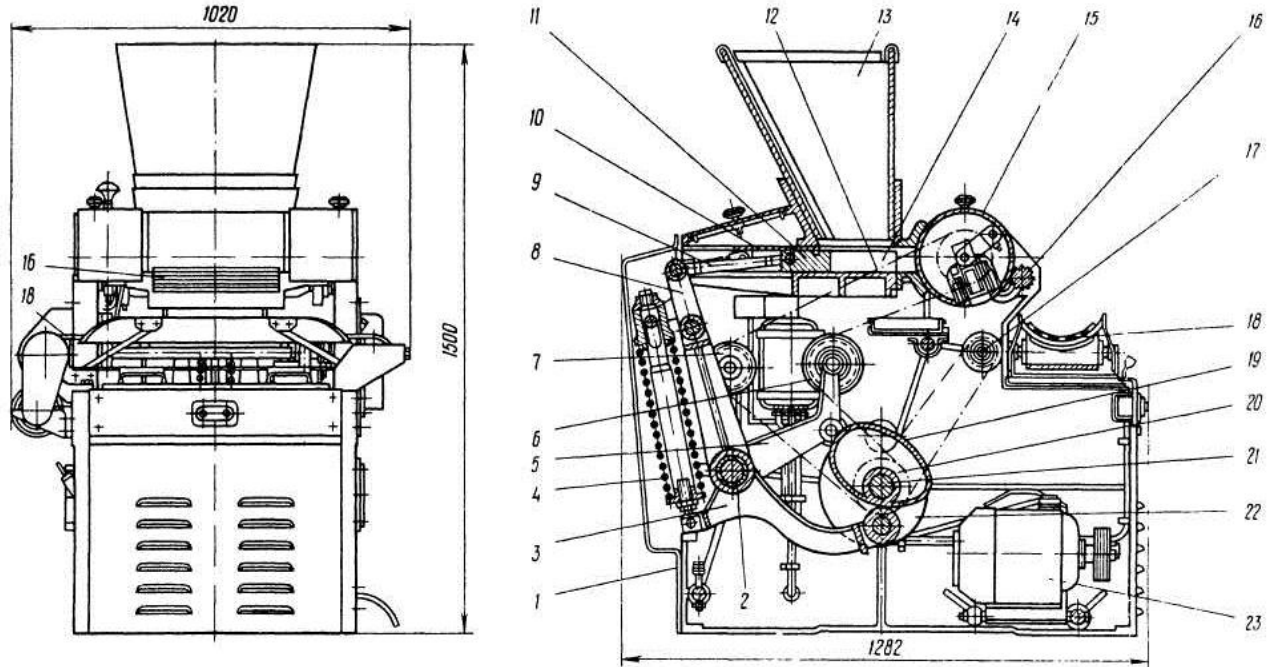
Тістоподільна машина РМК-60 з поршнеvim нагнітанням: 1 – станина; 2 – опорний вал; 3, 5, 8 – важелі; 4 – пружинний демпфер; 7, 6, 20 – зірочки; 9 – штанга; 10 – відсічна заслінка; 11 – нагнітальний поршень; 12, 15 – подільні головки; 13 – приймальна головка; 14 – подільник; 16 – розпушувальний валик; 17 – вал; 18 – транспортер; 19, 22 – кулаки; 21 – головний вал; 23 – електродвигун
